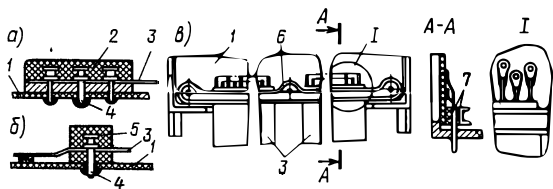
Крепление гибкого печатного кабеля переходной колодкой (а), планкой (б) и скобой (в): 1 — плата печатная; 2 — колодка; 3 — кабель гибкий печатный; 4 — крепежный штырь; 5 — планка; 6 — скоба; 7 — прокладка
